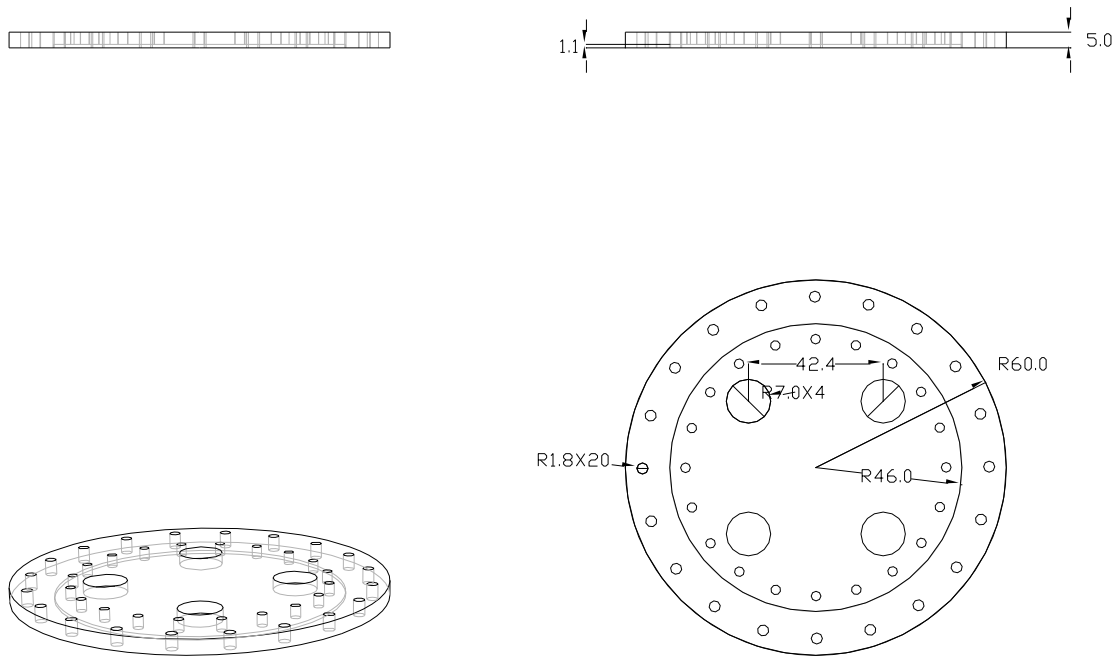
Planimetría placa inferior SHIELD ⁵⁶
